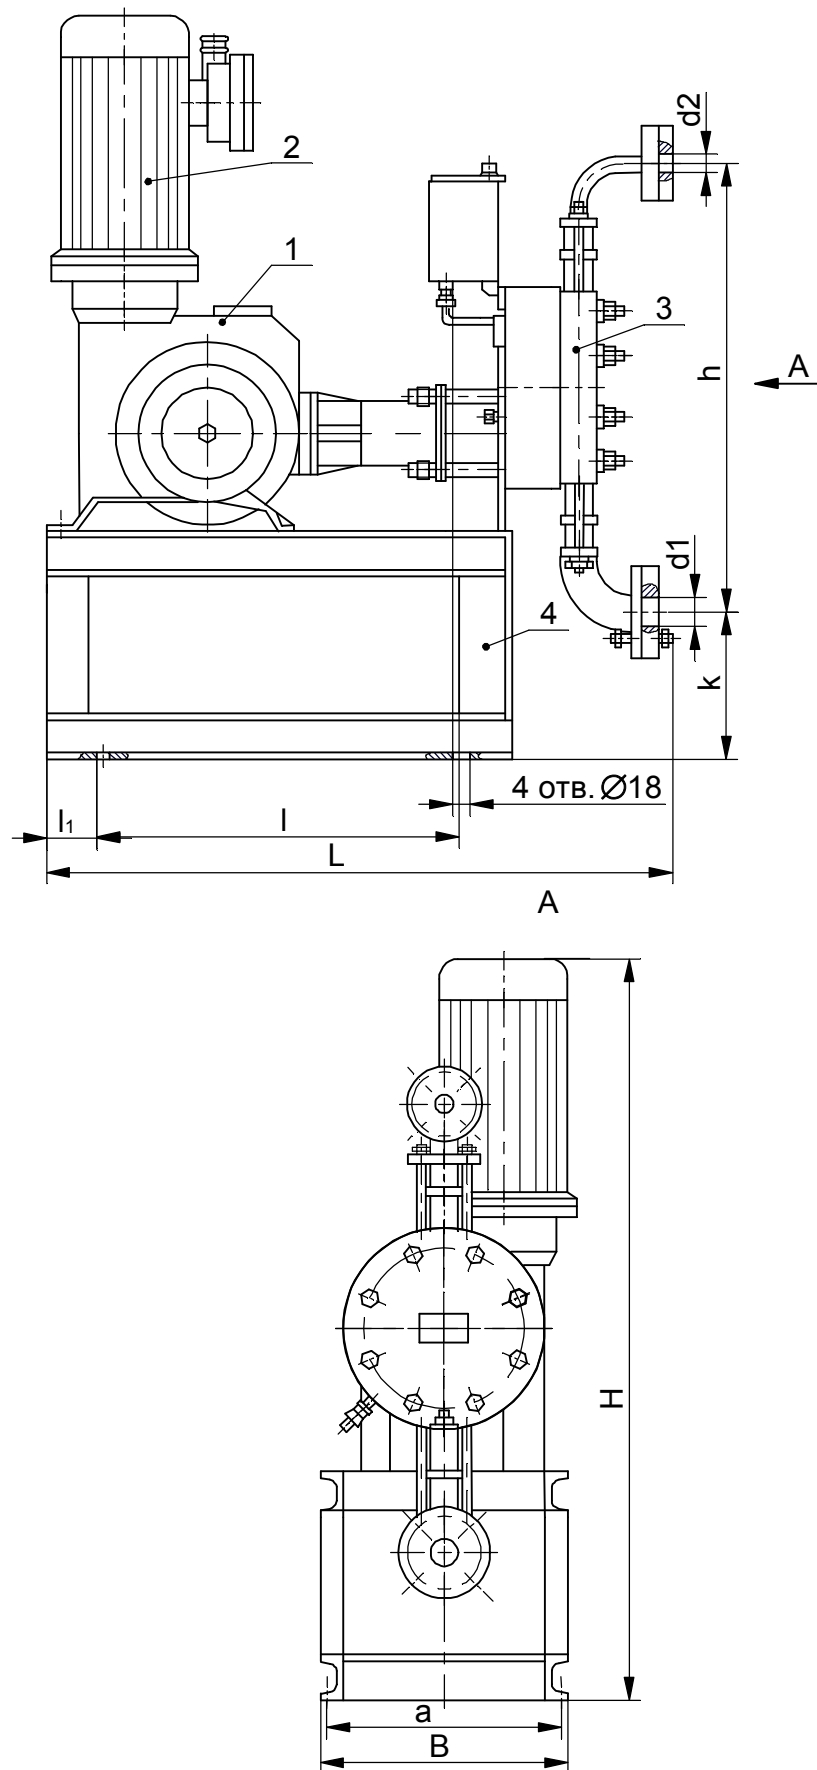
Внешний вид агрегата с параметрами номинального режима 1000/16; 1600/16; и 2500/10. Габаритные и установочные размеры
